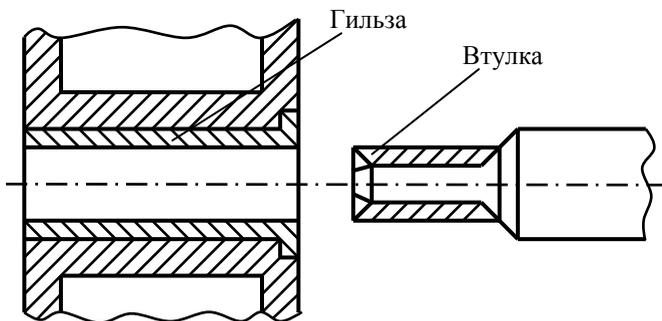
Схема способа постановки дополнительной ремонтной детали
